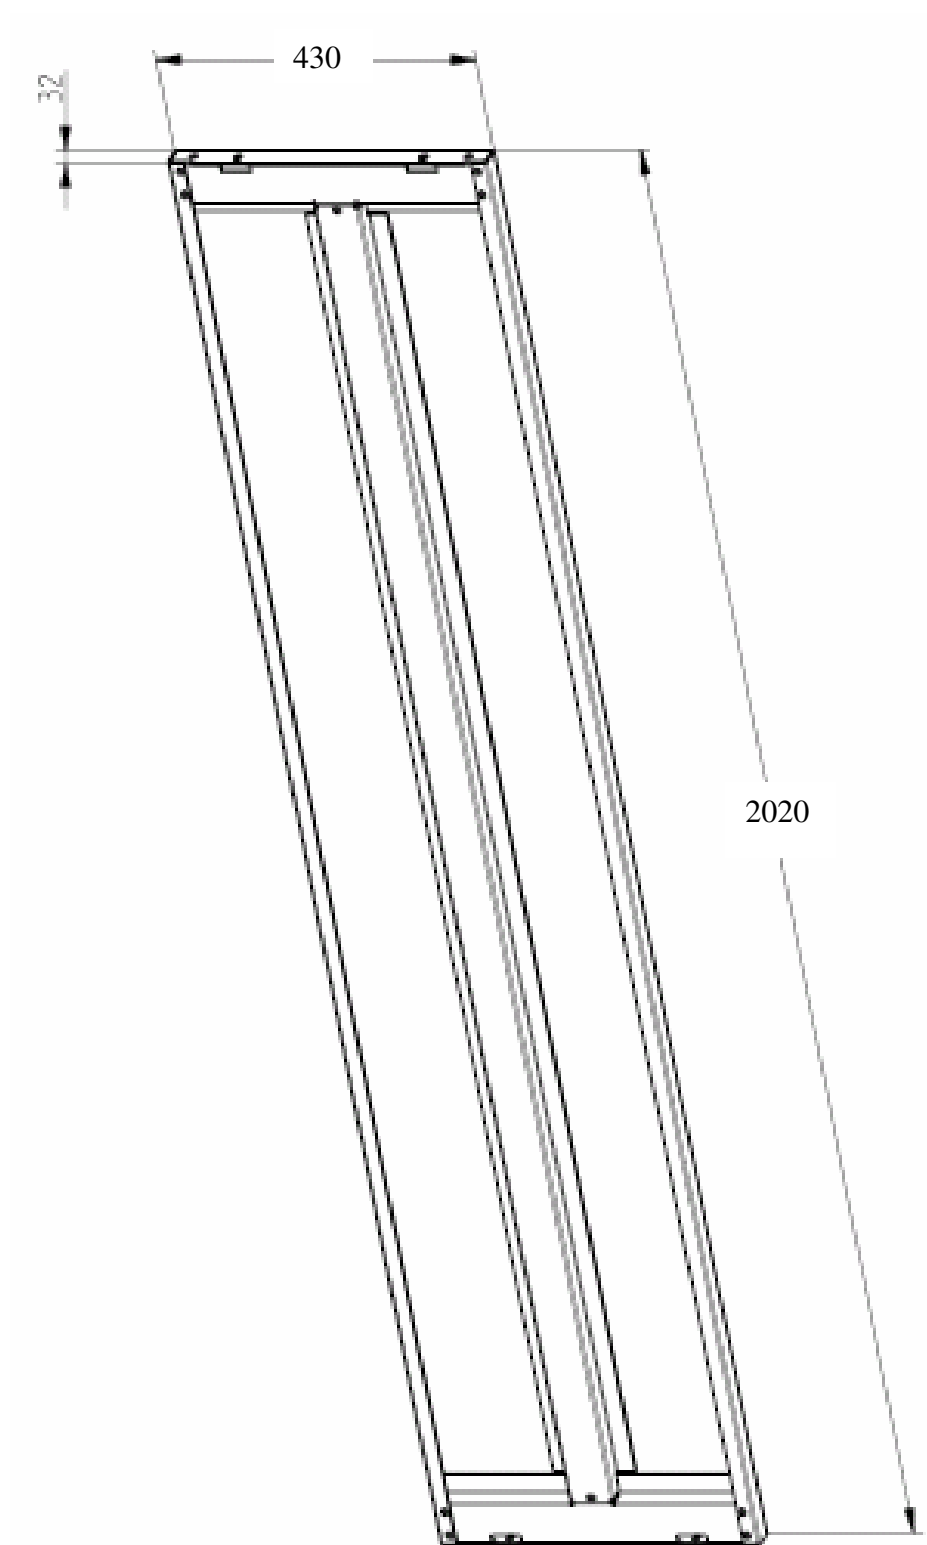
Esquema do conjunto painel colado e rebitado (dimensões em mm)
